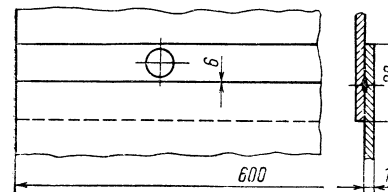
Шов роликовой сварки. Шири-
